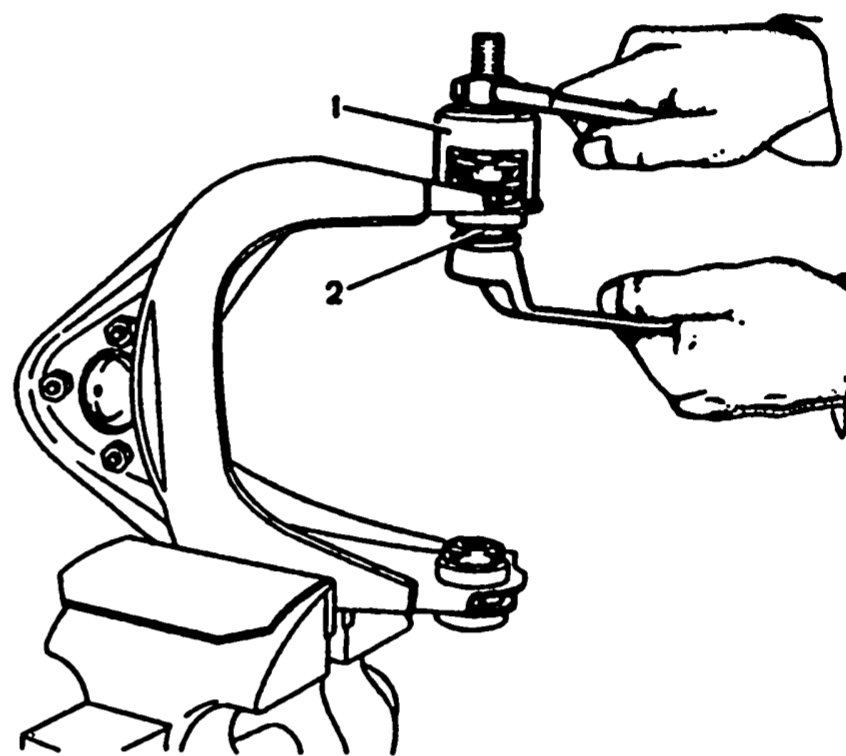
Выпрессовка шарниров верхнего рычага: 1 - приспособление А.47046; 2 - шарнир
